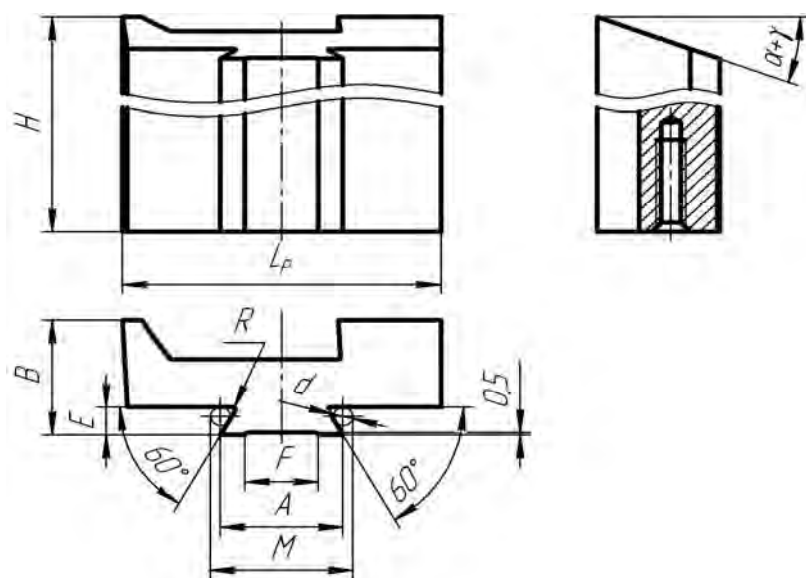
Габаритные и присоединительные размеры призматических фасонных резцов
